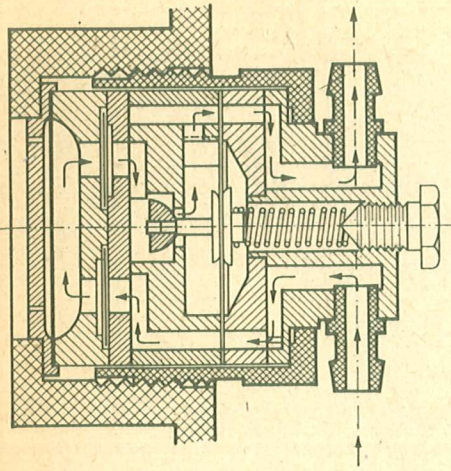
HB-Membranpumpe mit Druckregler im Schnitt
